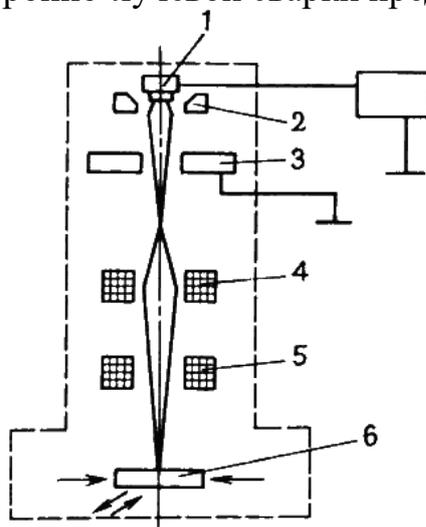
Схема установки для электронно-лучевой сварки
